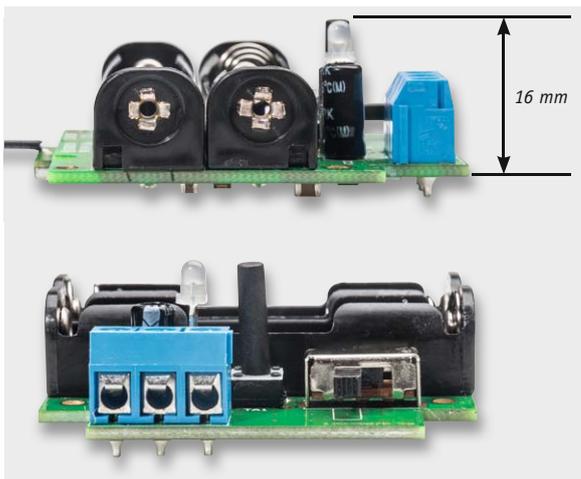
Komplette mit den bedrahteten Bauteilen bestückte Platine
